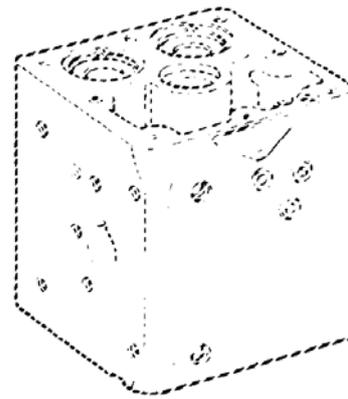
Покомпонентный чертеж силового корпуса PGA
